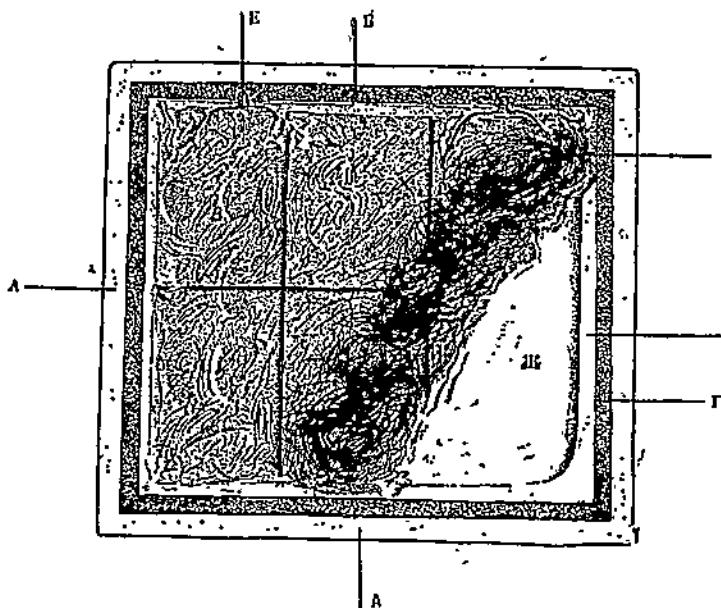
Отливка рельефа на пеньке. А — кожух, Б — kleевая форма, В — первый слой гипса, Г — пенька, Д — второй слой гипса, Е — петля для подвешивания.
